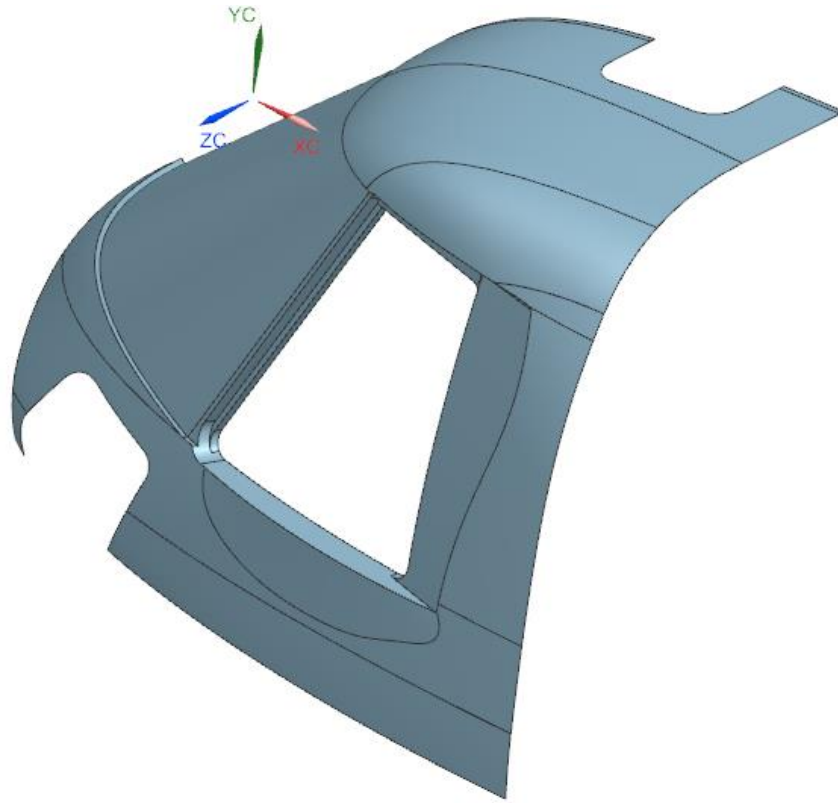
Поверхность внешней обшивки фонаря кабины пилотов с подсечкой под установку лобового остекления
